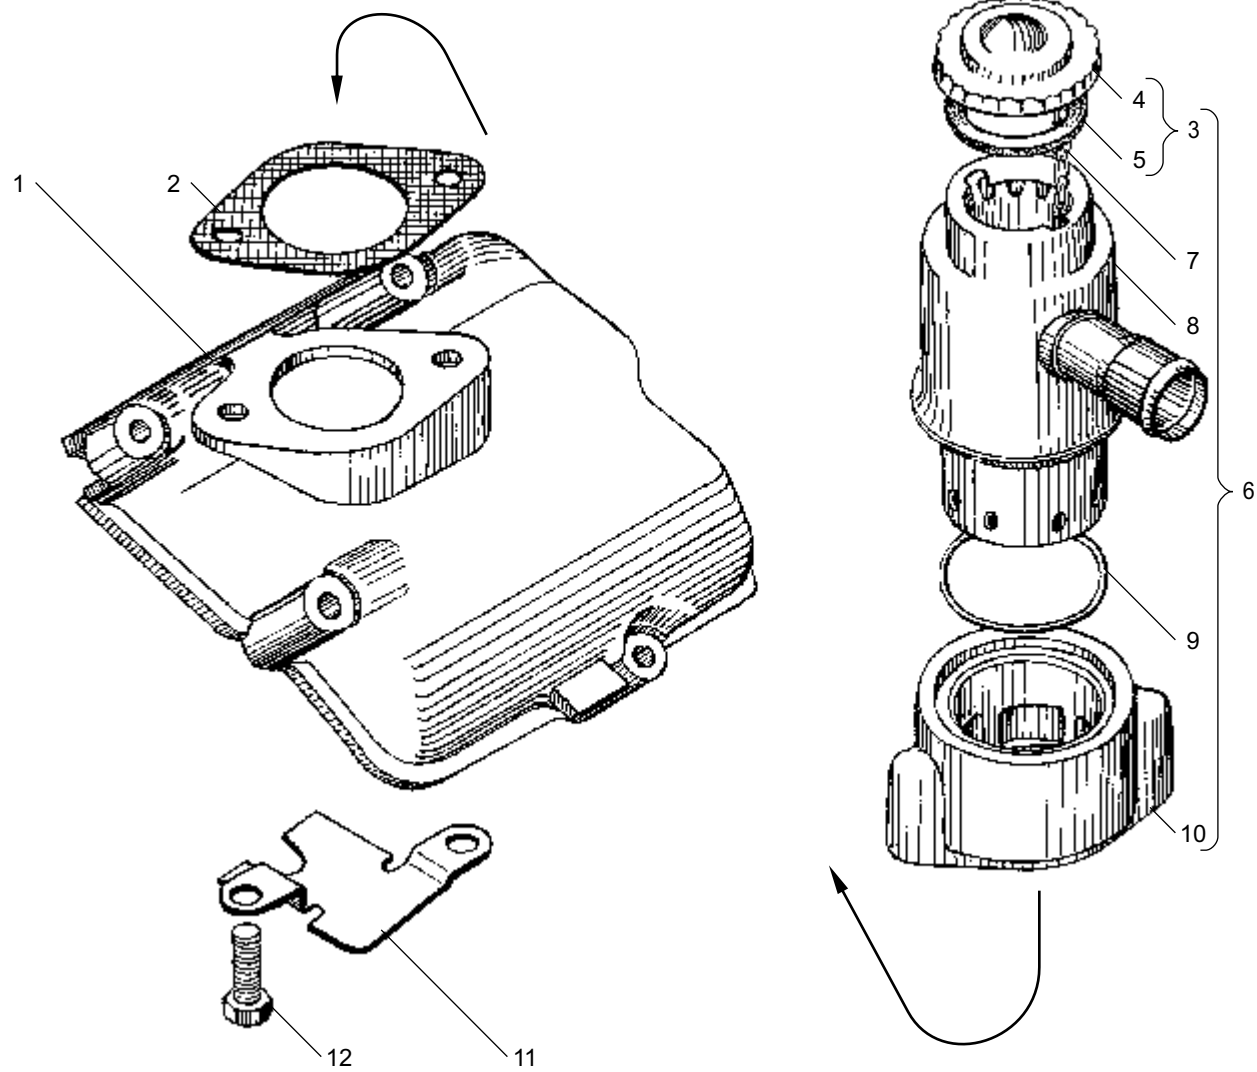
ВЕНТИЛЯЦИЯ КАРТЕРА двигателей с индивидуальными головками
